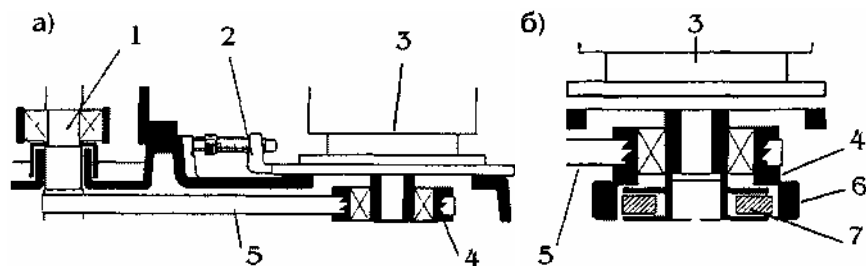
Плоскоременная передача (а) и фрикционная муфта (б). 1-вертикальный вал сепаратора; 2-приспособление для натяжения ремня; 3-электродвигатель; 4-шкив; 5-плоский ремень; 6-фрикционная муфта; 7-подушки фрикционной муфты.
